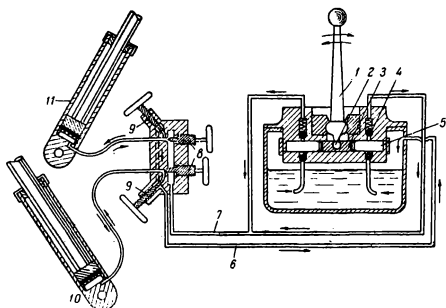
Схематический чертеж снегоочистителя Д-151.
